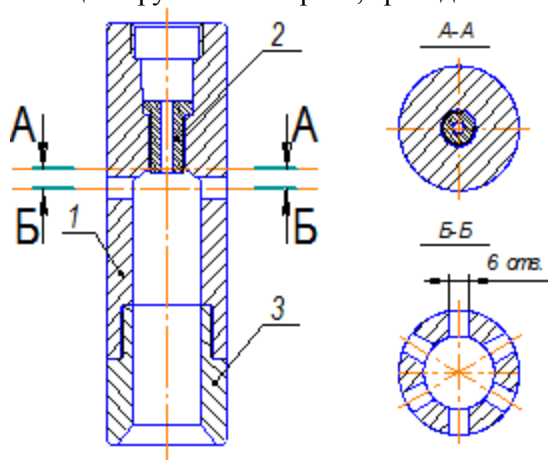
Струйный аппарат гидромониторно-эжекторного долота: 1 – корпус аппарата, 2 – сопловая насадка, 3 – насадка с диффузором
